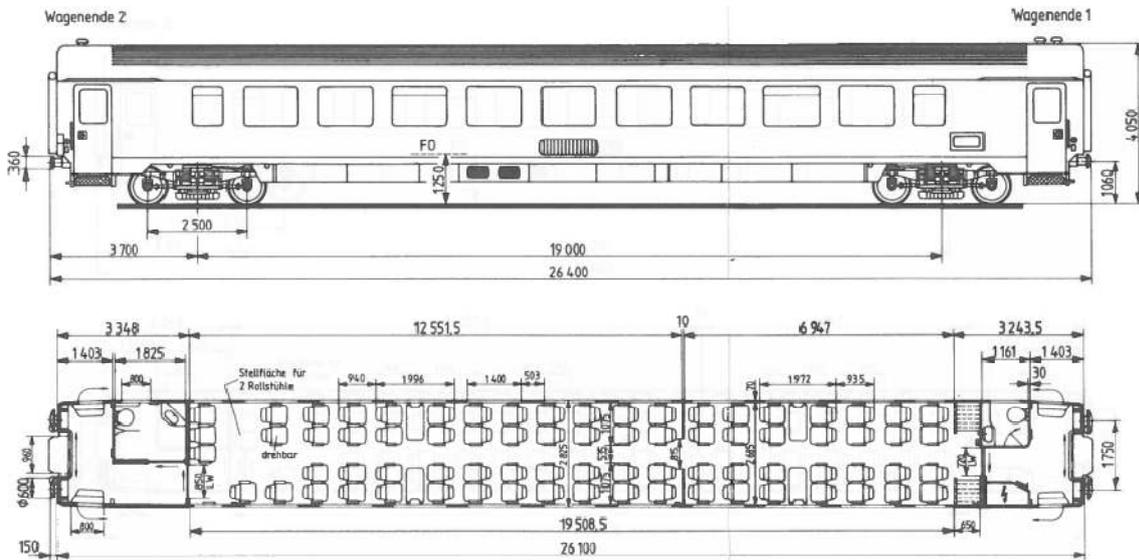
Grundriss und Seitenansicht Bpmz 294.x
